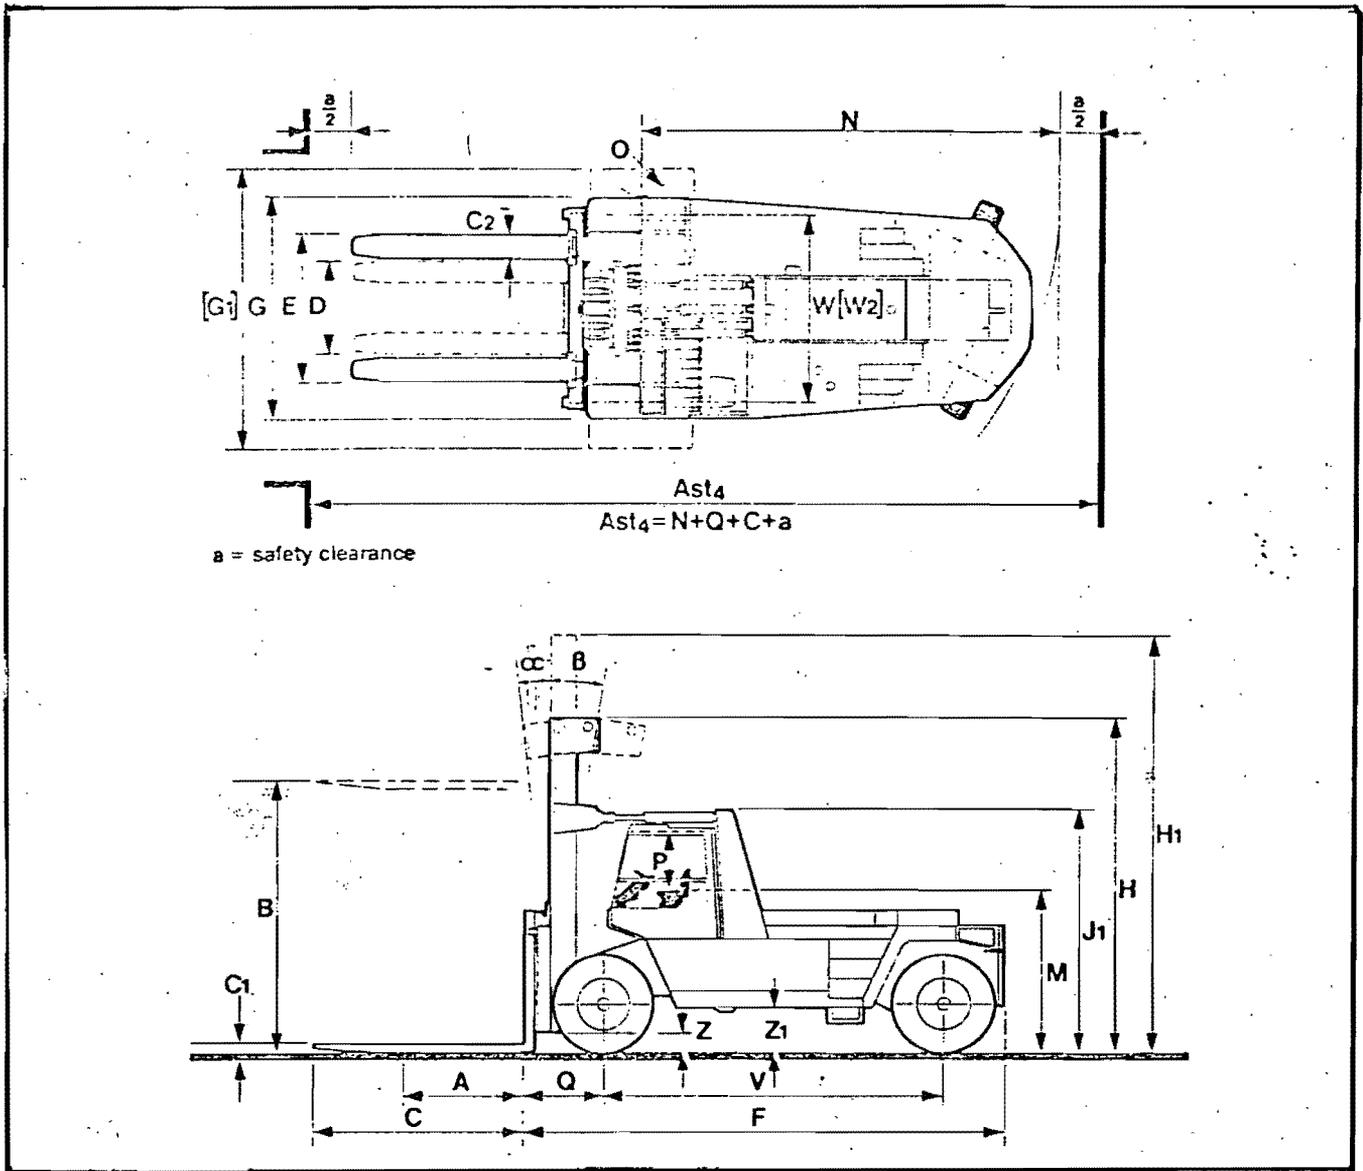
DIMENSIONES PRINCIPALES DE MONTACARGAS
